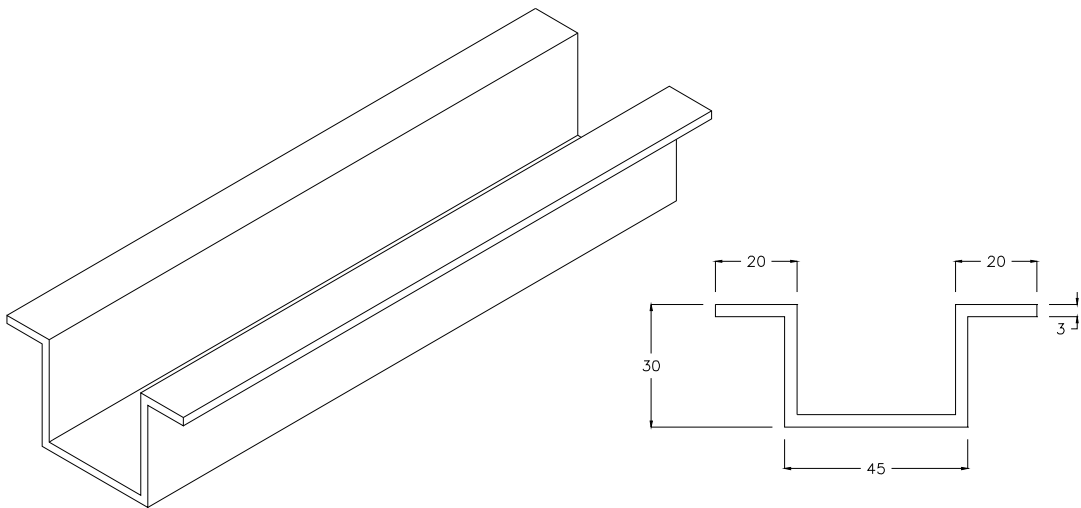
Emboîtement étanchéité associée - Boîtier de liaison
